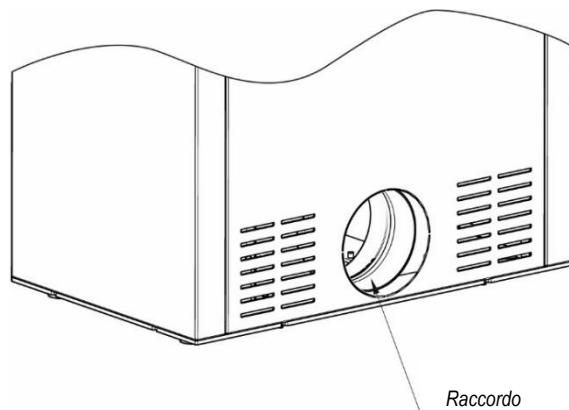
Connessione alla stufa AIR WOOD verso la presa d'aria esterna - versione dal fondo dell'apparecchiatura.
